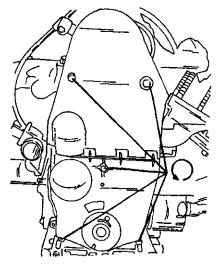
Стрелками указано расположение болтов крепления защитного кожуха зубчатого ремня.
